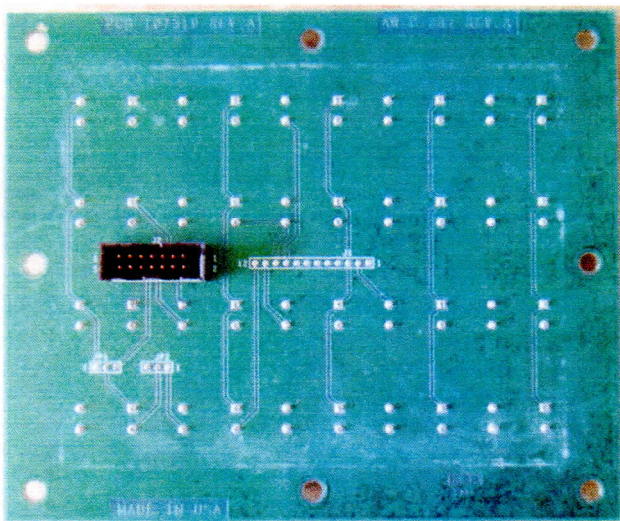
Tarjeta Local Preset identificada con número de parte 107520 revisión A vista cara de Soldaduras.
